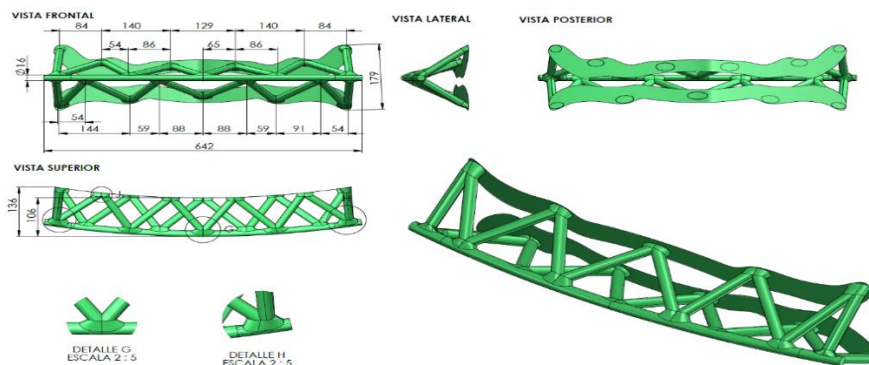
Dimensiones de probeta para ensayo de compresión, largo 642 mm, ancho máx. 136 mm, alto 179 mm
